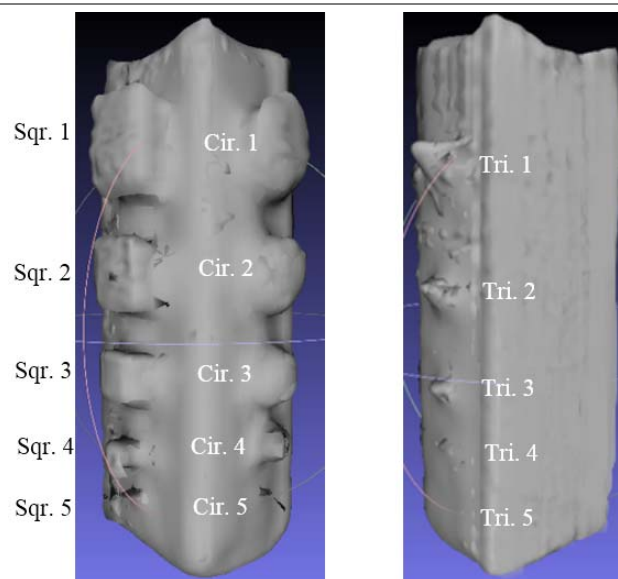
Prueba de figuras geométricas: Diseño CAD (a) y pieza impresa (b).
